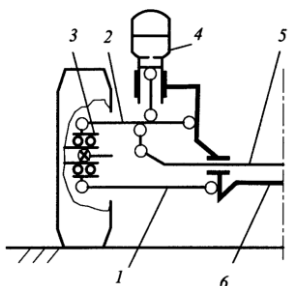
Схема передньої підвіски з поперечною ресорою одноточкового кріплення:
